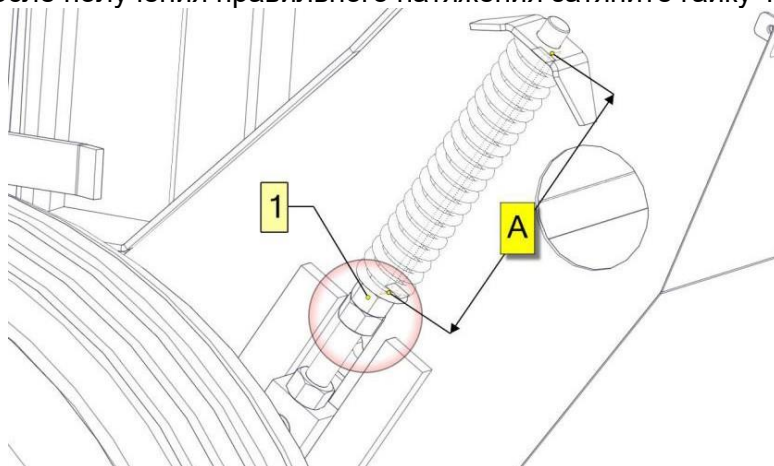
Регулировка натяжения цепного пруткового транспортера пресс-подборщика Z587
